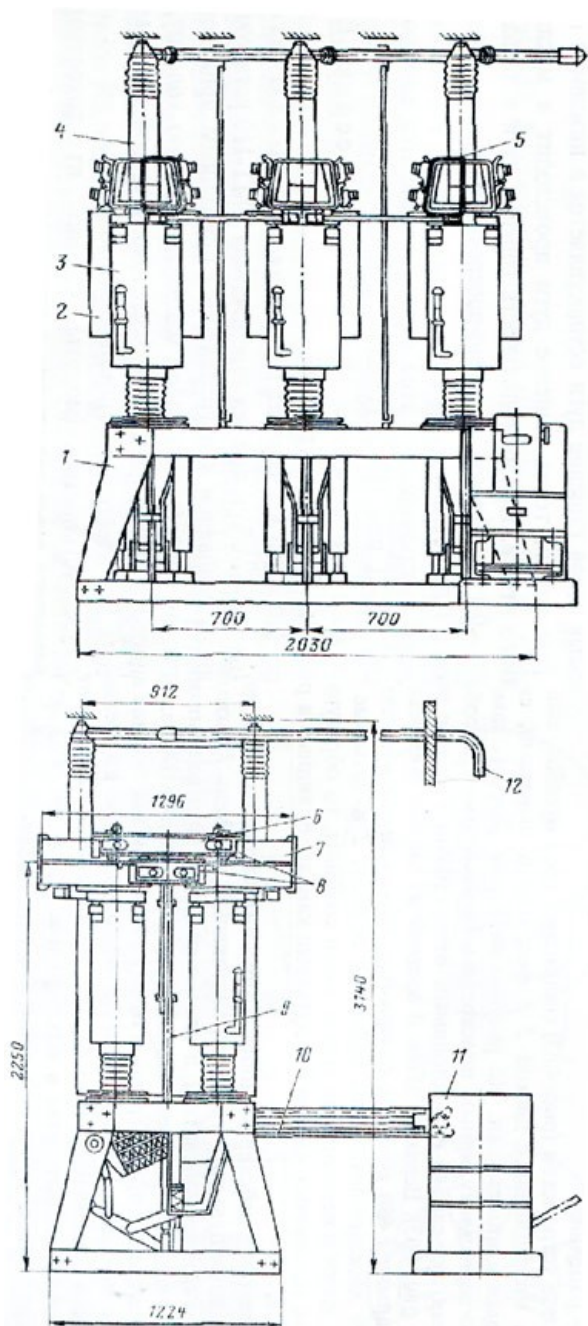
Выключатель ВГМ-20/11200УЗ: 1 - основание; 2 - межполюсная перегородка; 3 - бак; 4 - маслоотделитель; 5 - магнитопровод; 6 - траверса; 7 - вывод для присоединения шин; 8 - ножи главных контактов; 9 - штанга; 10 - тяга к приводу; 11 - привод; 12 - выхлопной конец газоотвода
